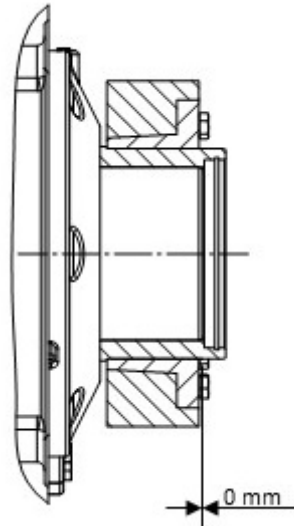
Montage van de massieve machineas bij speciale holle assen met krimpschijf
